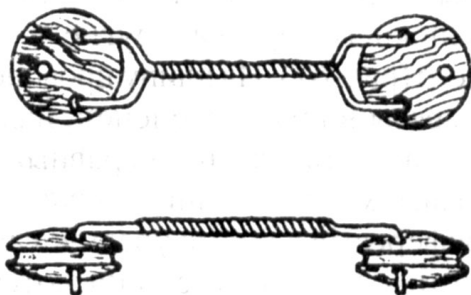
Приспособление для установки юферсов на одинаковом расстоянии
